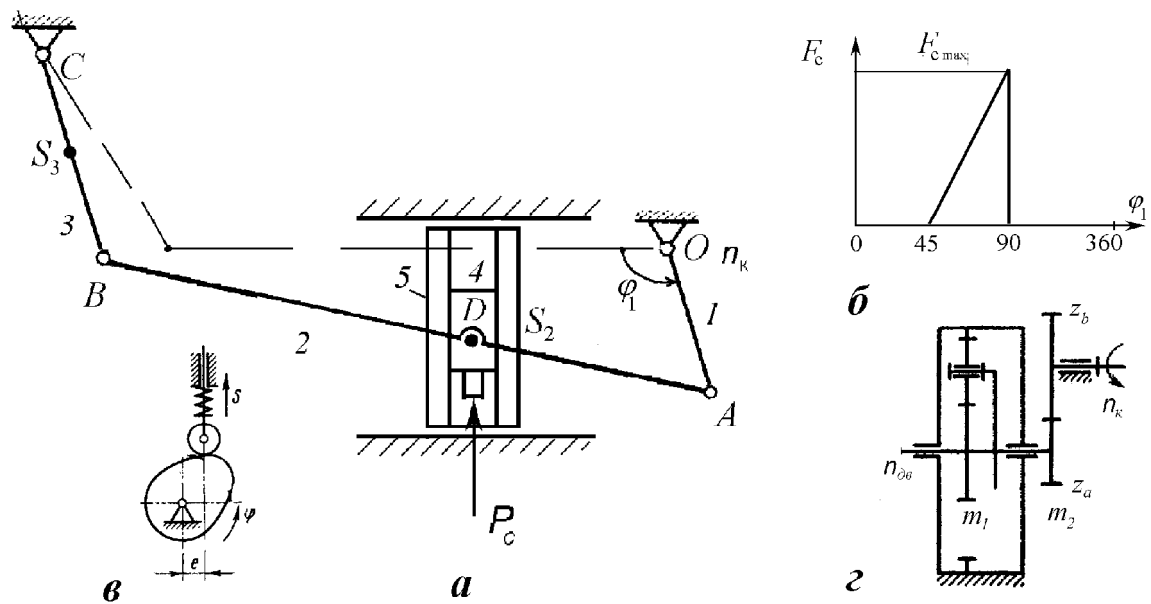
На схеме: а- рычажный механизм привода ползуна 4 с пуансоном; б- диаграмма силы сопротивления; в- кулачковый механизм привода ножа для резки заготовки; г-привод рычажного механизма.
